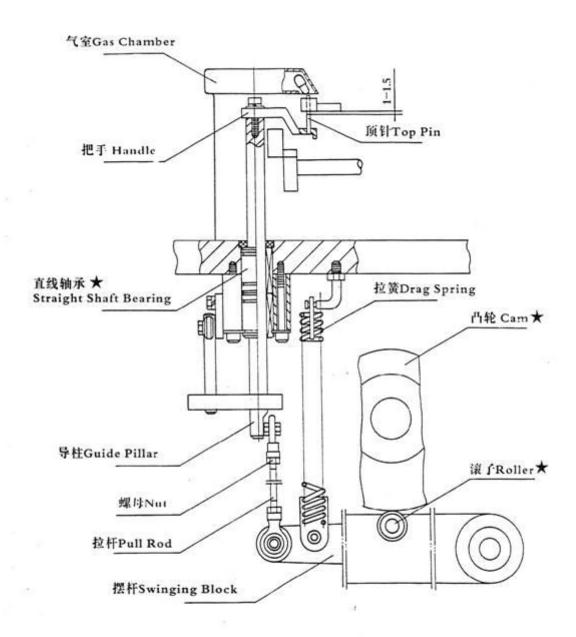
剔囊机构 Figure15 Capsule Trimming Mechanism
